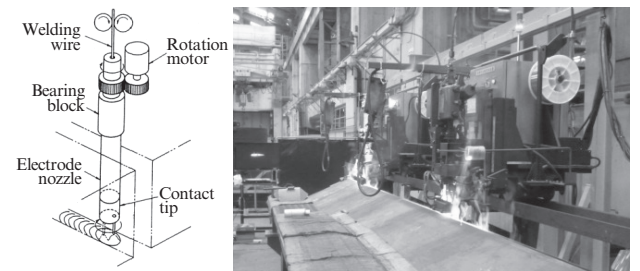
狭開先溶接法の原理とタンデム無監視溶接状況
